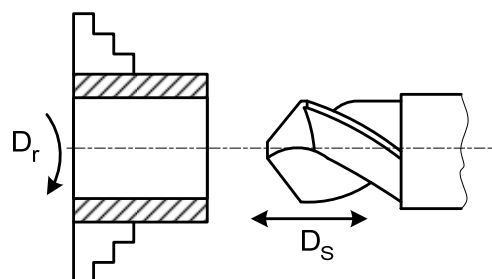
Вторая схема операции сверления: обрабатываемая деталь вращается; сверло имеет осевую подачу
